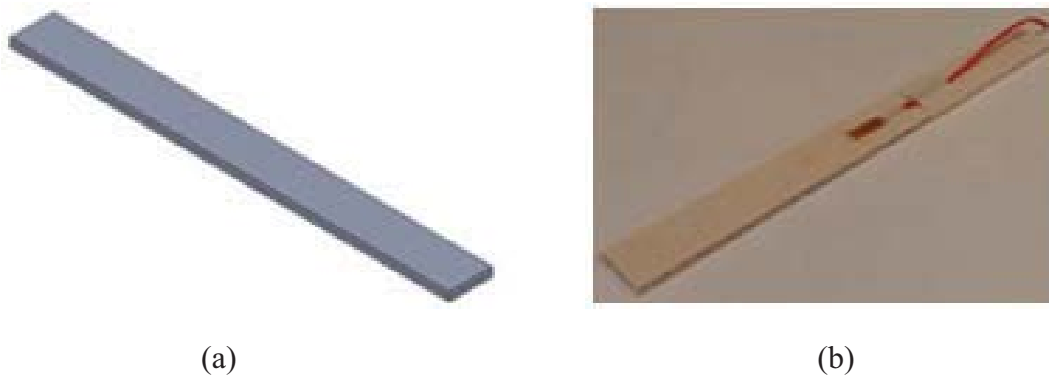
(a) Modelo 3D con SolidWorks® de la probeta uniaxial; (b) Probeta uniaxial con galga pegada.
